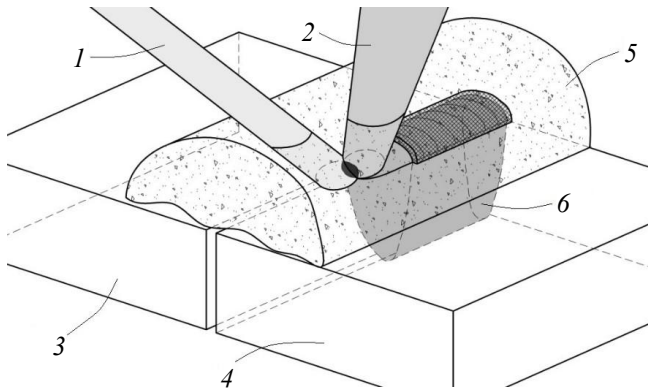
Условная схема процесса лазерной сварки по слою флюса
